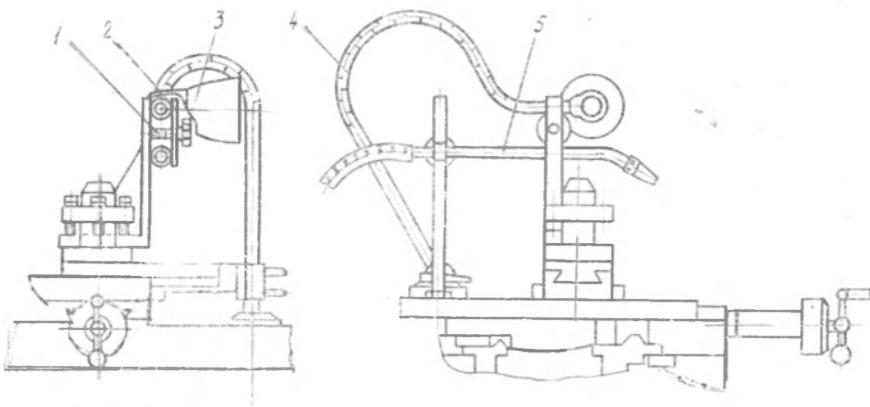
Схема зажимов для походного положения станка ИТ-1М.
